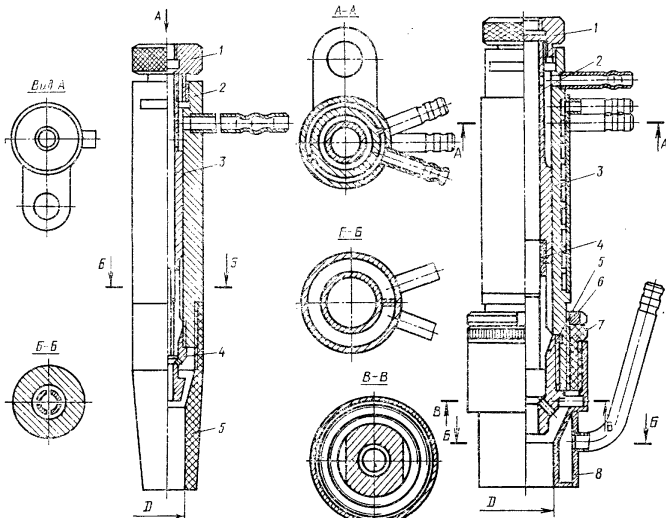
Сварочная горелка типа ГНА-040:
